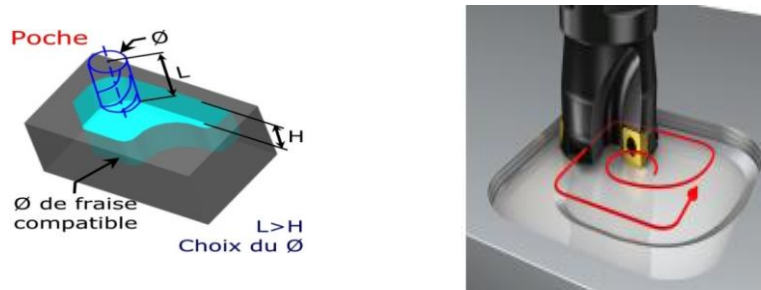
Schéma d'élargissement d'une cavité/poche.
